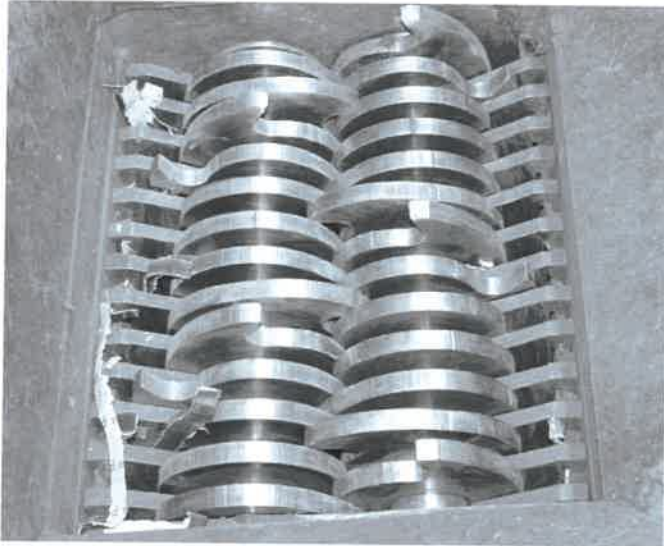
Schneidwerkzeuge der verwendeten Rotorschere.
